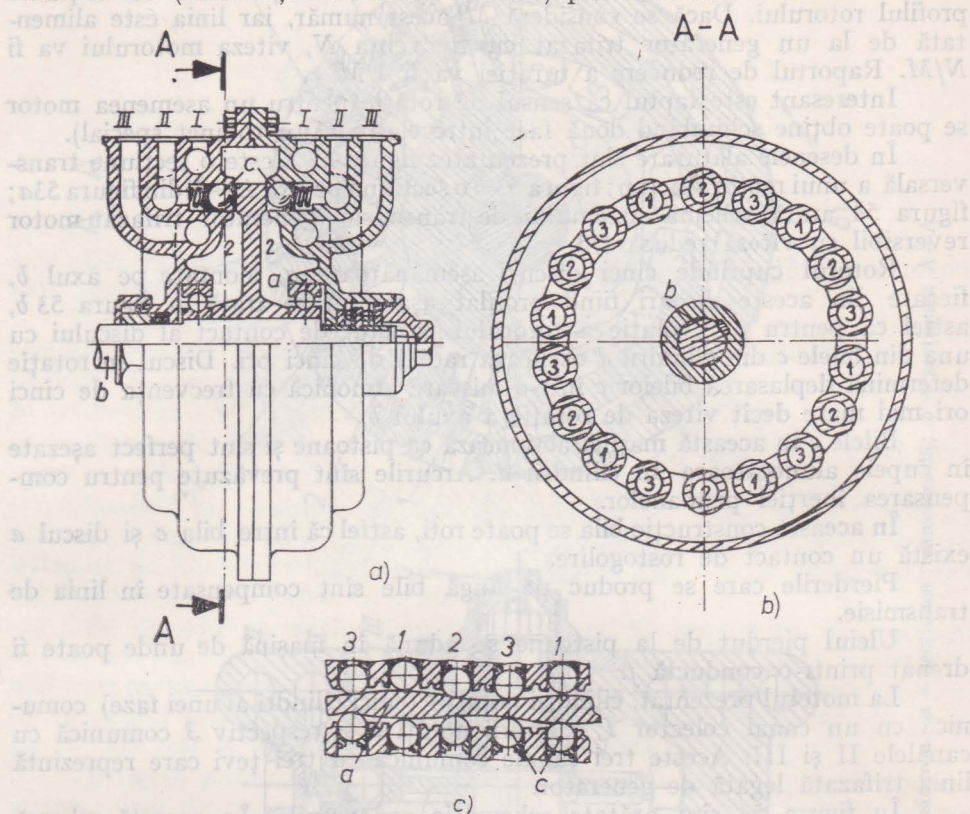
Motor sonic cu cilindri statorici axiali pe ambele părți ale rotorului:
